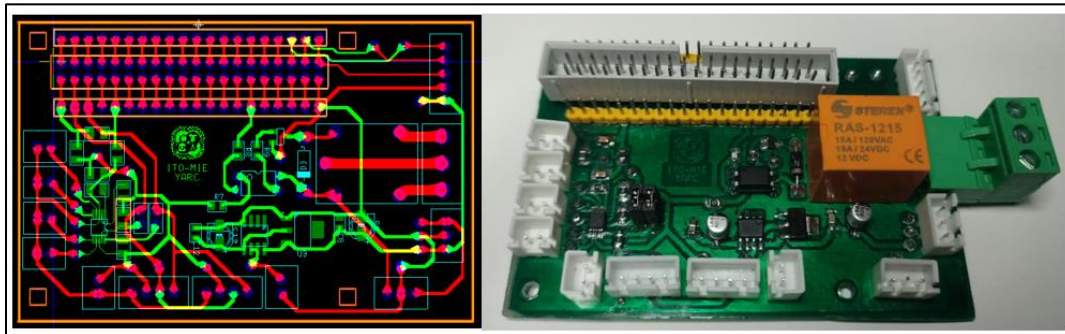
Diseño y manufactura de circuito módulo complementario de Raspberry pi 4.
